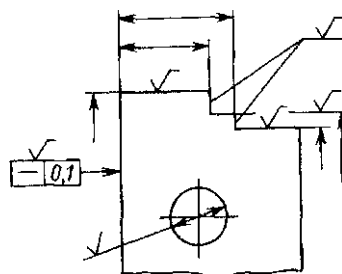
Нанесение обозначений шероховатости поверхности на изображении изделия
